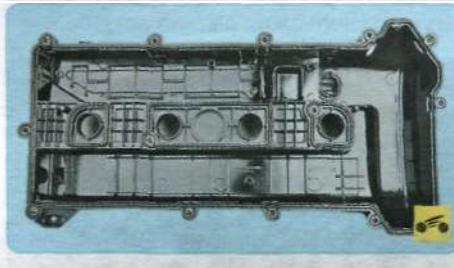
Порядок затяжки болтов крепления крышки головки блока цилиндров двигателя 2,0 Duratec TИVCT
